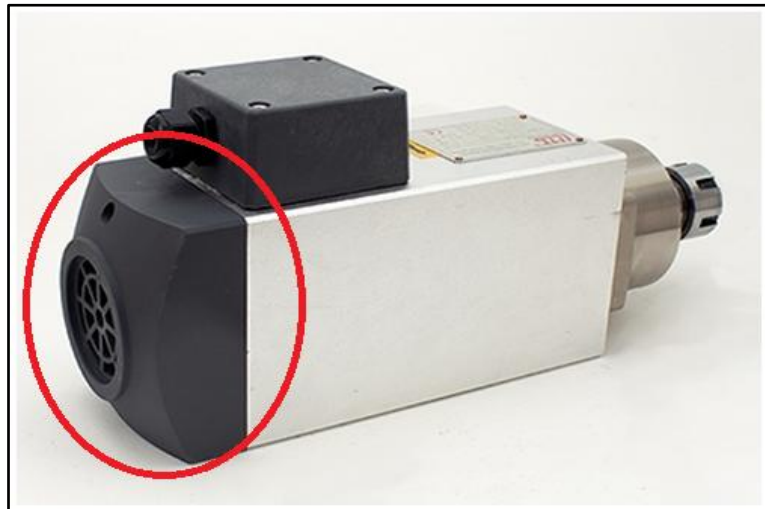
GMT AIR COOLED CNC SPINDLE
